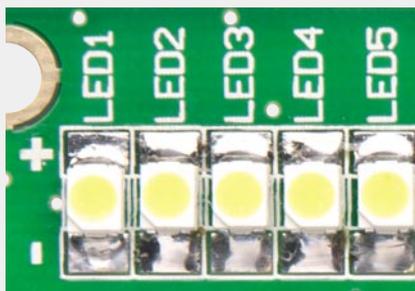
Bestückung mit SMD-LEDs, direkt auf die Platine gelötet
